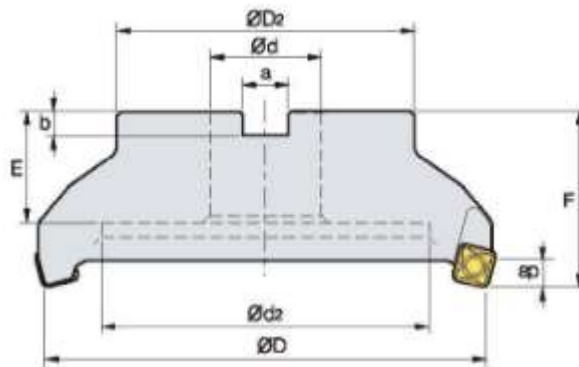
Чертеж и таблица размеров торцевой фрезы
